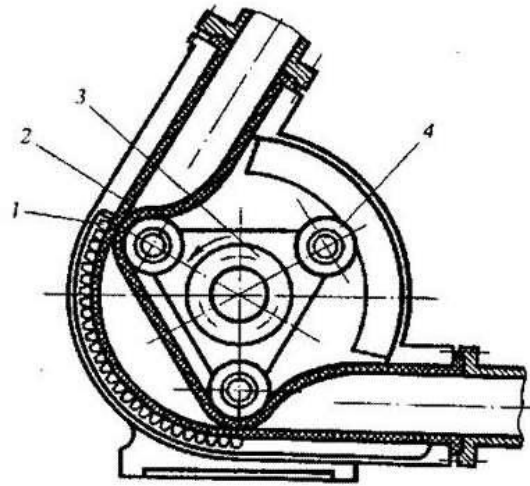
Схема серійного шлангового насоса: 1 – корпус; 2 – шланг; 3 – тримач; 4 – ротор з роликами.
